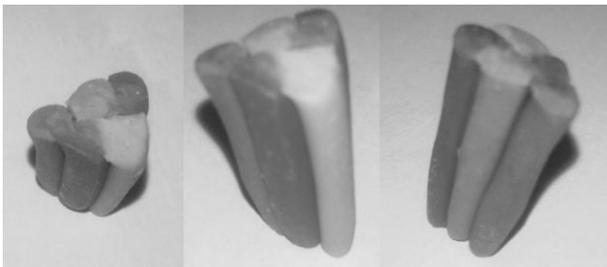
Заготовка из столбцов разноцветного пластилина
